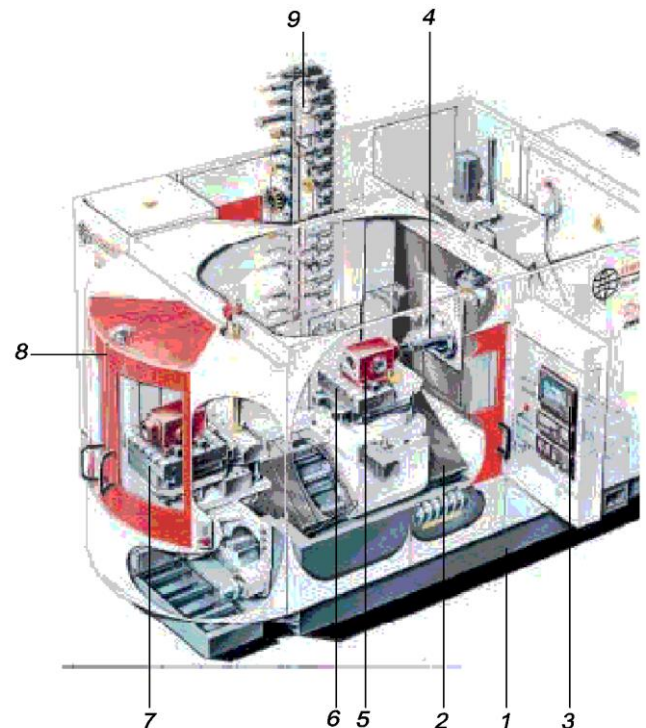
Обробний центр мод. CWK 500 фірми Starrag Heckert: 1 – станина; 2 – конвеєр для стружки; 3 – система управління; 4 – шпиндель; 5 – заготовка; 6 – стіл-супутник; 7 – супутник з заготовкою; 8 – екран; 9 – магазин
